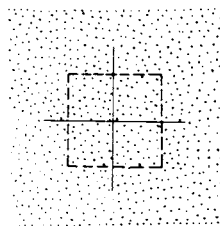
Обозначение рисок и контуров отверстия для бруска
